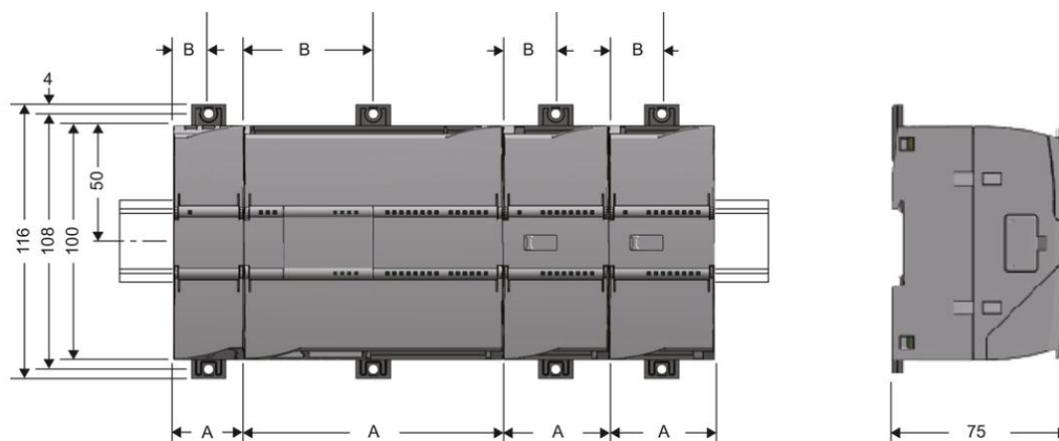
Dimensiones de montaje del Esclavo S7-1200 CM 1242-5
